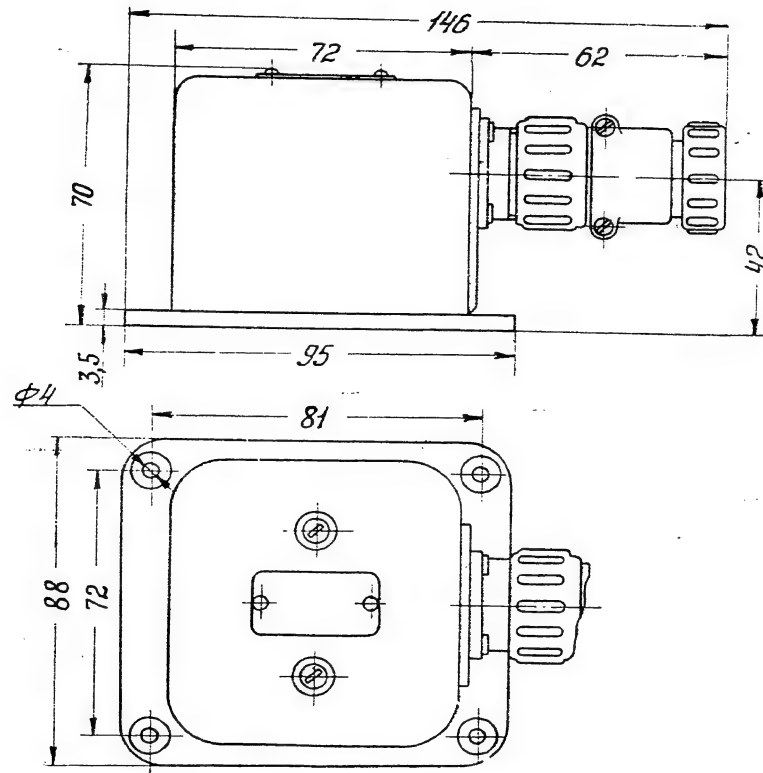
Габаритные размеры понижающего трансформатора ТРП-52
